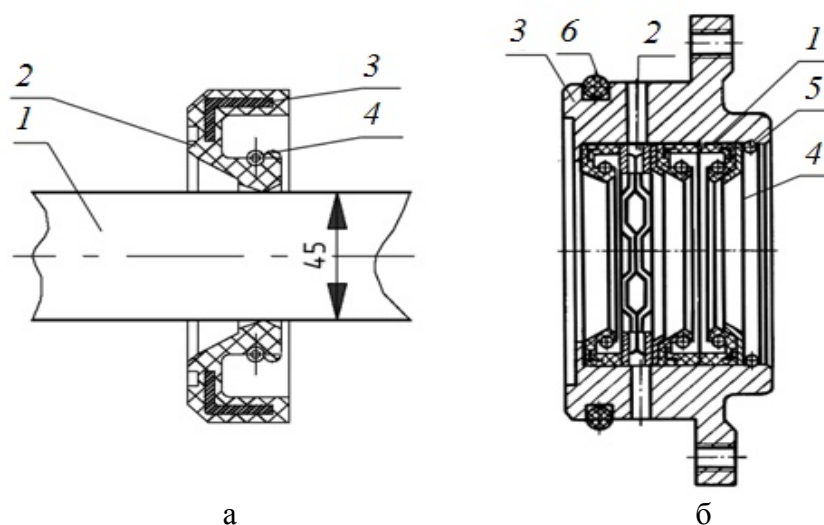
Уплотнительный стакан: а: 1 – вал насоса; 2 – манжета; 3 – стальной каркас; 4 – пружина; б: 1 – манжета; 2 – кольцо; 3 – корпус; 4 – упорное кольцо; 5 – стопорное кольцо; 6 – резиновые кольца
